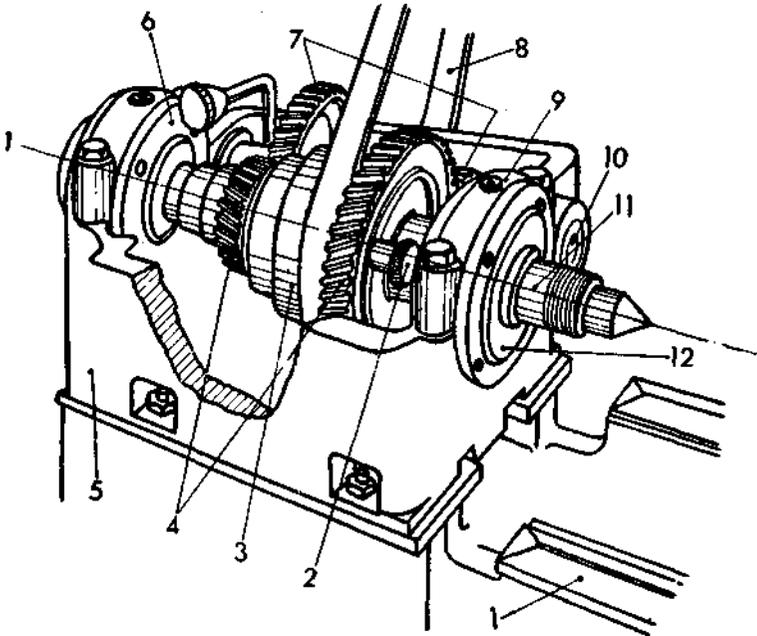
Cabezal de torno sencillo de cilindrar.— 1. Bancada. — 2. Pivote de arrastre. — 3. Cono de poleas. — 4. Engranaje del eje principal. — 5. Cuerpo del cabezal. — 6. Tapa portacojinetes. — 7. Engranajes del eje de reducción. — 8. Correa. — 9. Tapa fijación eje. — 10. Eje de reducción. — 11. Eje principal.— 12. Tapa del cojinete.
